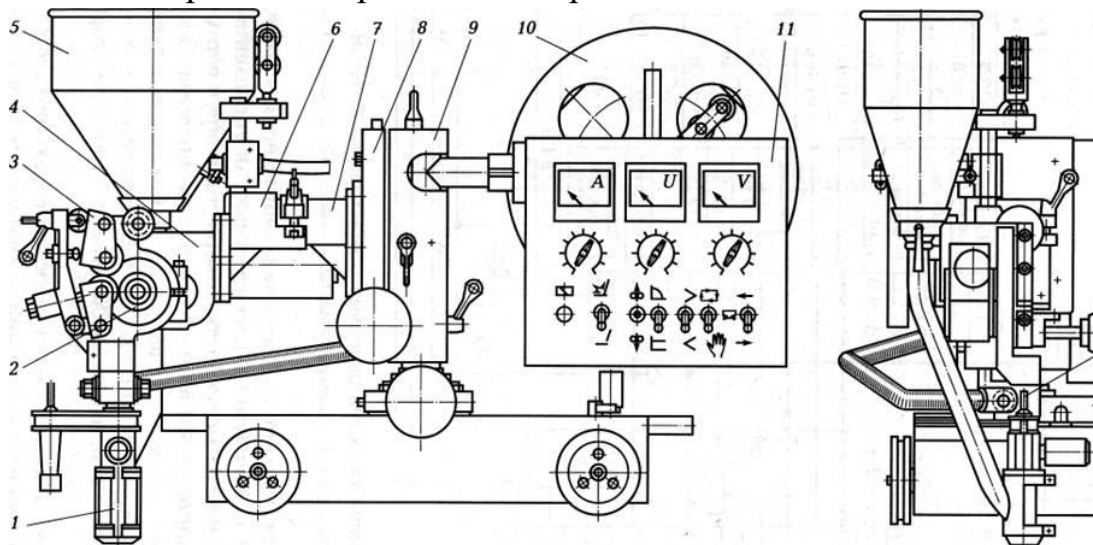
Сварочный трактор АДФ-1202
